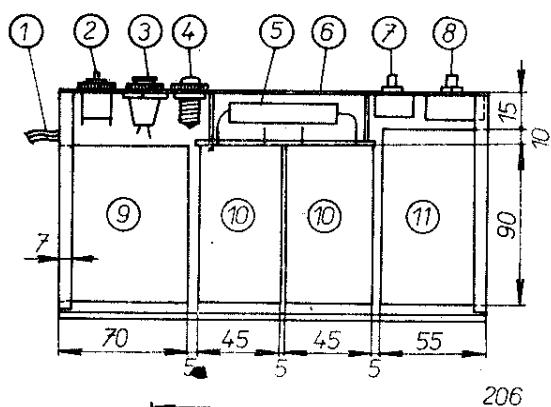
Šasi pro zesilovač ACC-10 W.
